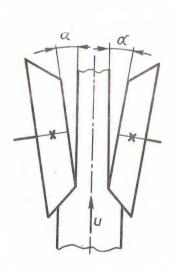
Схема установки торцово-конических фрез фрезернобрусующего станка.
